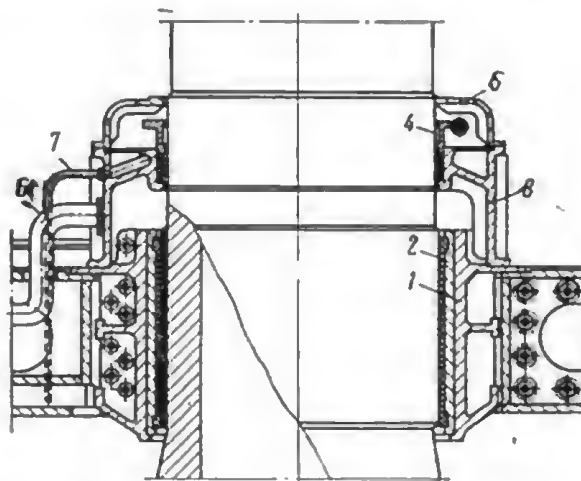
Узел подшипника с резиновым вкладышем.
